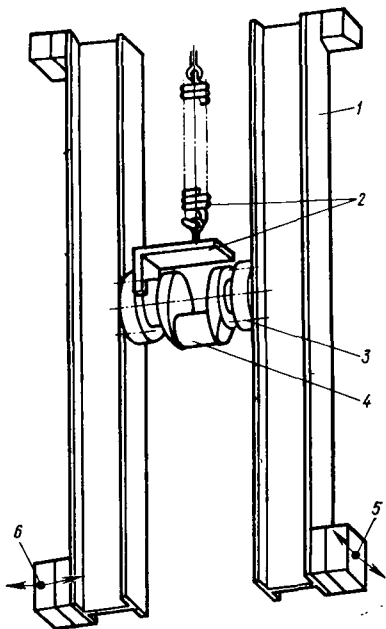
Схема стэнда для испытаний коленчатых валов:
